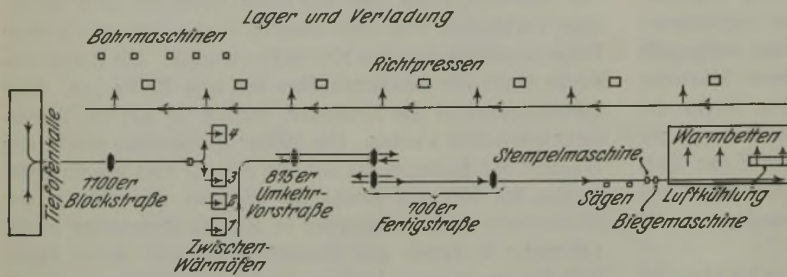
Blockstraße und Schienenwalzwerk der Bethlehem Steel Co. in Steelton.
